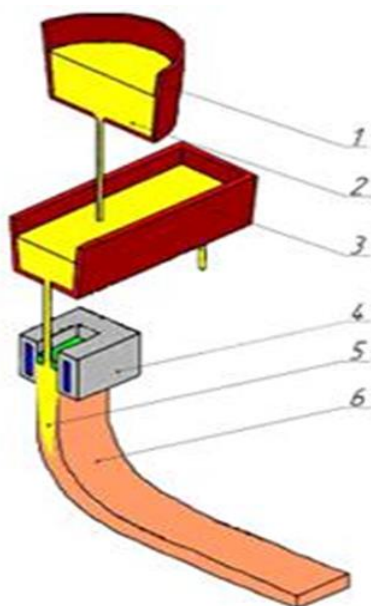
Схема отримання слябової заготовки при безперервній розливці металів на МБЛЗ: 1 – ківш для розливки металу; 2 – метал, що розливається; 3 – проміжний ківш; 4 – кристалізатор; 5 – рідка лунка металу у заготовці; 6 – безперервнолита заготовка-сляб
